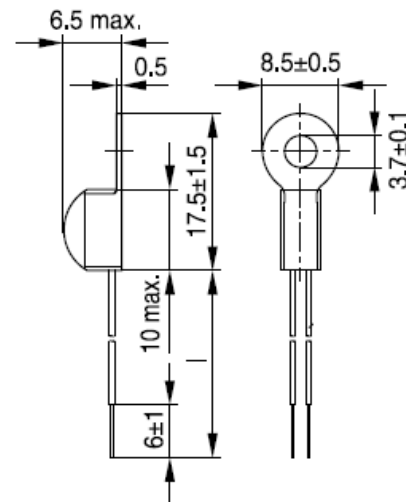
Внешний вид и габаритные размеры NTC-термистора B57703M
